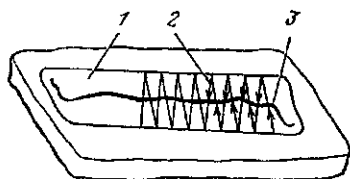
Схема зачистки поверхности вокруг трещины перед заваркой: 1 — зона зачистки; 2 — направление движения шлифовального круга; 3 — трещина
